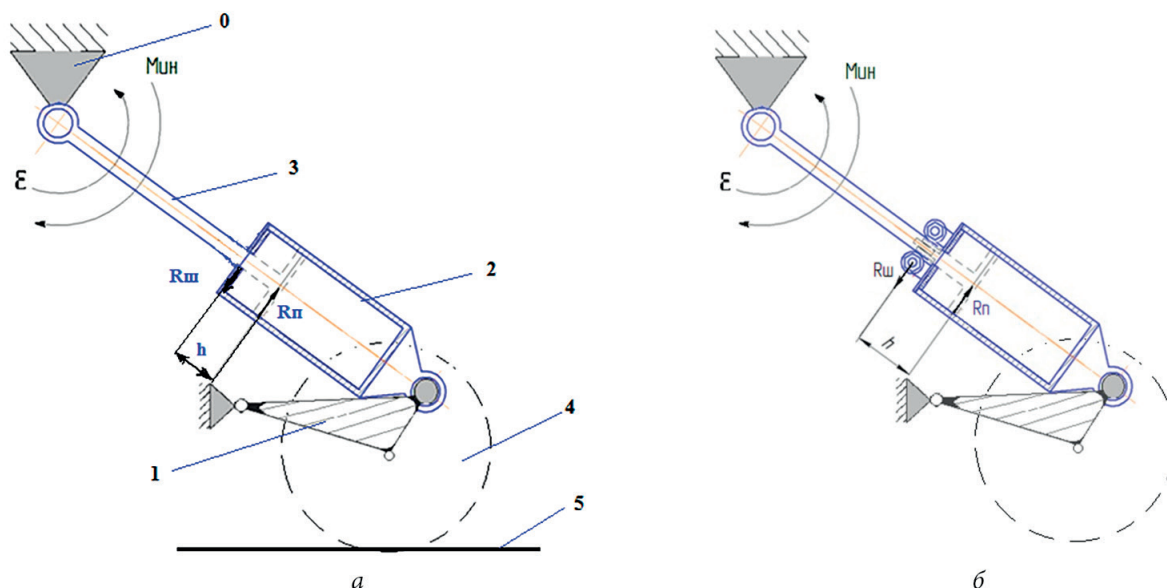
а — кинематическая схема механизма подвески без разгружающего устройства: 0 — корпус машины, 1 — баланси́р, 2 — корпус гидроамортизатора, 3 — шток, 4 — каток, 5 — гусеница; б — кинематическая схема механизма подвески с разгружающим устройством
